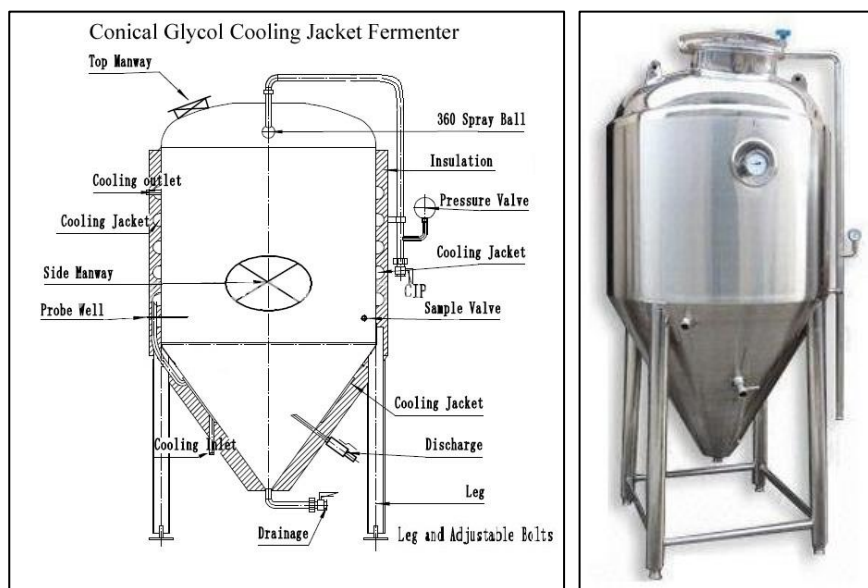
Esquema de un fermentador (Fuente: jnrainbowmachinery.com)
